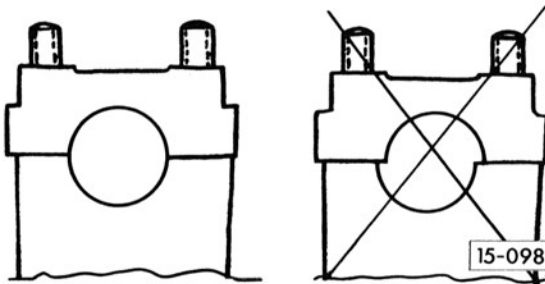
Einbaulage Lagerdeckel-Nockenwelle
